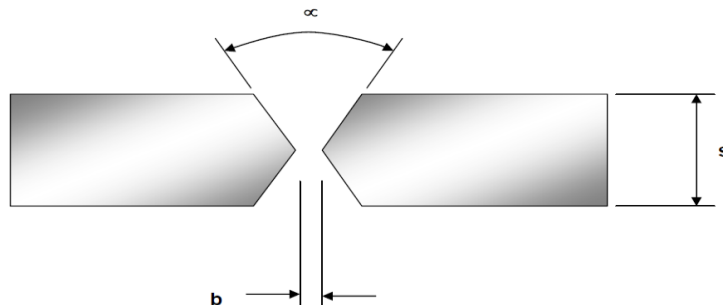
Soldadura de Bisel en V sencilla.
